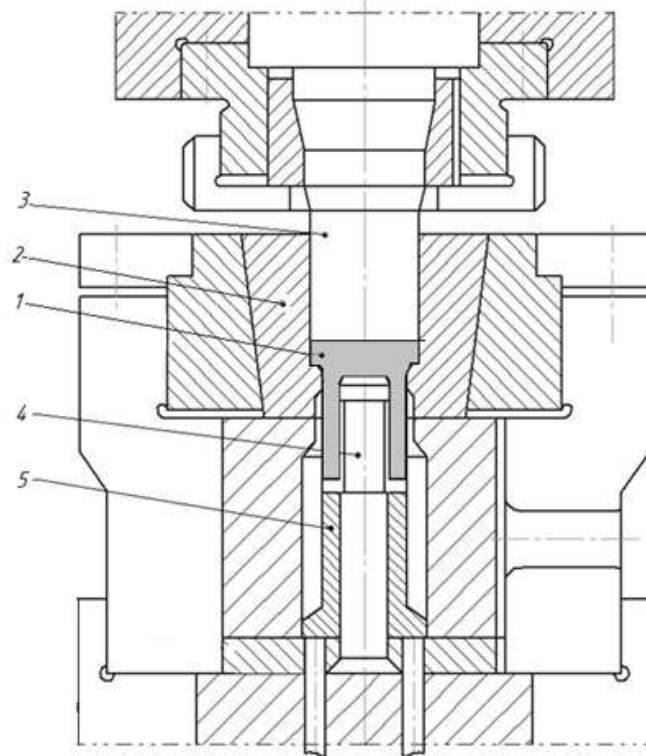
Схема штампа для прямого видавлювання з контрпуансоном: 1 – деталь; 2 – матриця; 3 – пуансон; 4 – контрпуансон; 5 – виштовхувач
